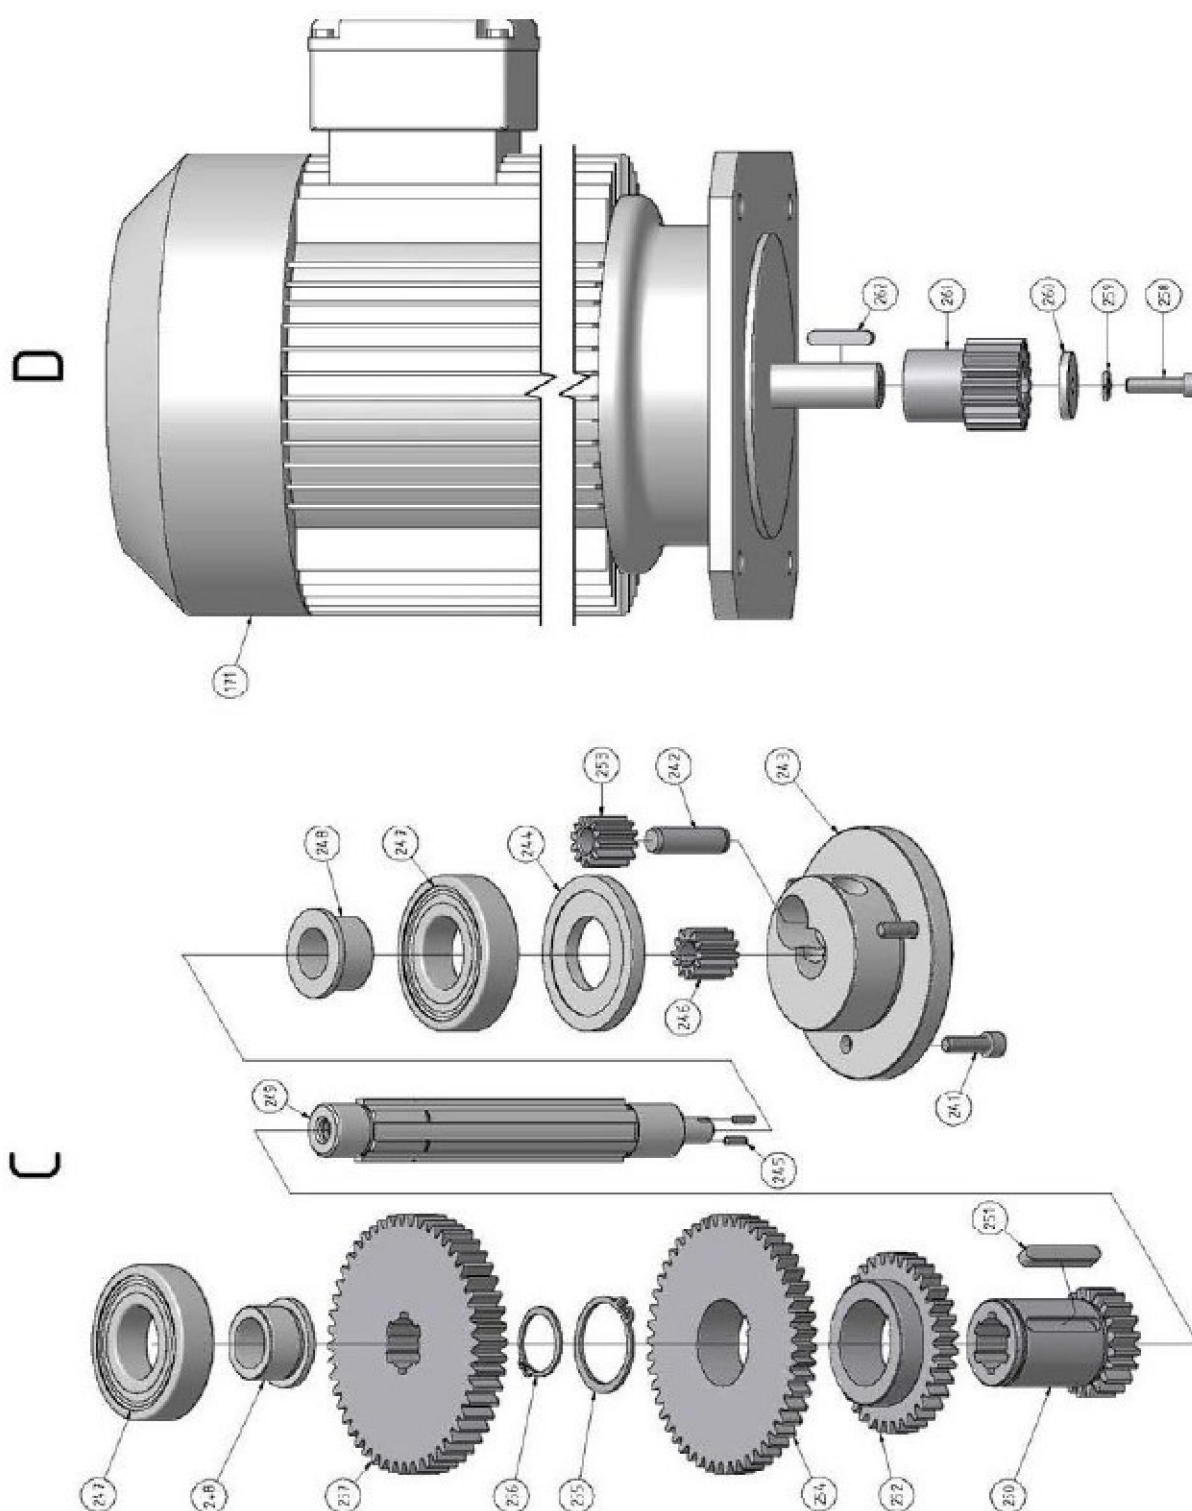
husillo principal caja de engranajes 2 de 4 - Gear box main spindle 2 of 4
